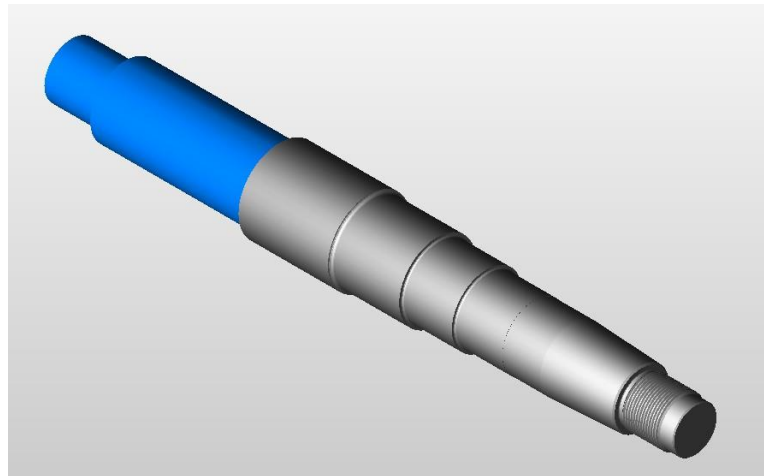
Установ А. Вид обробленої поверхні
